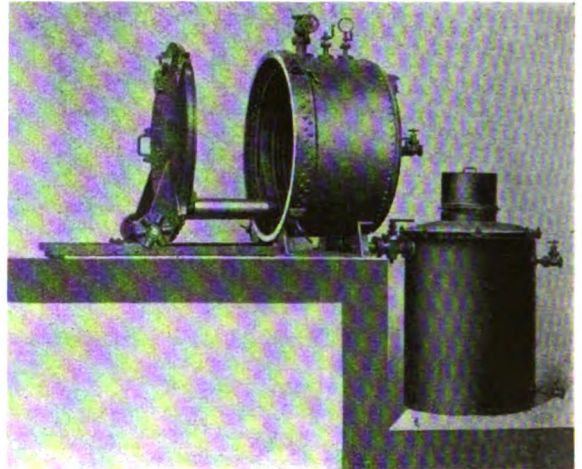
Kabel-Trocken- und -Tränkgeläß mit Massebehälter.
